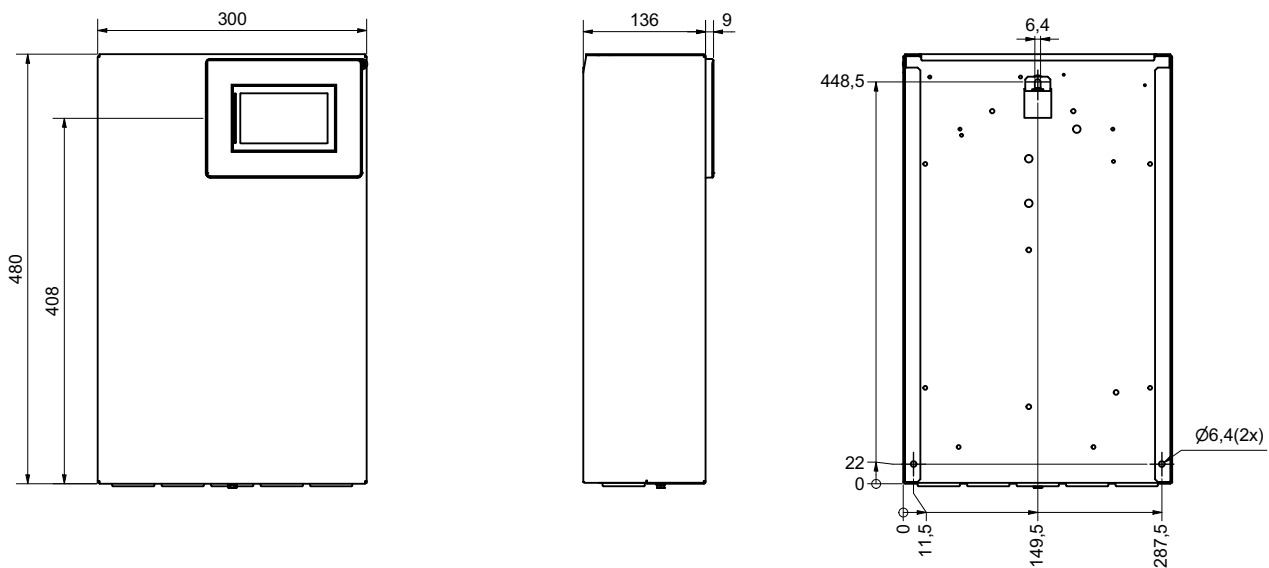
Dimensions du régulateur maître mural de chauffage
